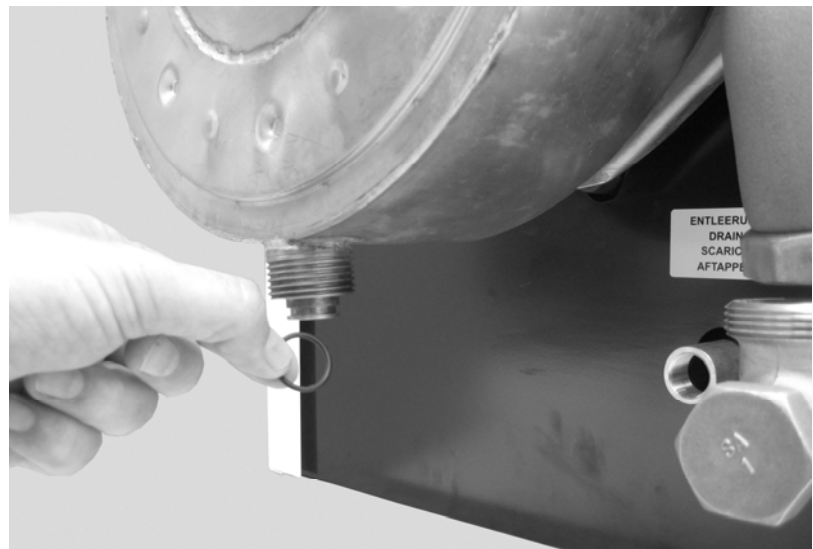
Montage des O-Ringes 17x2 mm (95.99287-0094) am RWT.
